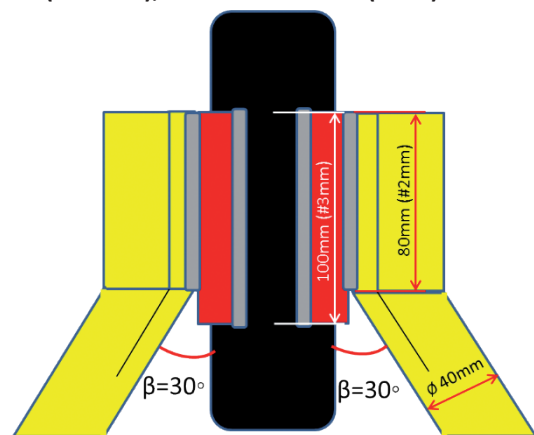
Esquema da ferramenta de estampagem do tubo lateral e moldagem.
